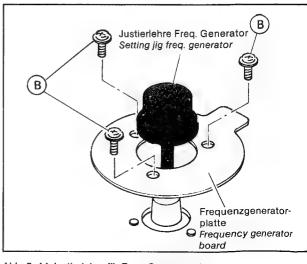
Justierlehre für Freq. Generatorplatte Fig. 2–14 Frequency generator board setting jig
